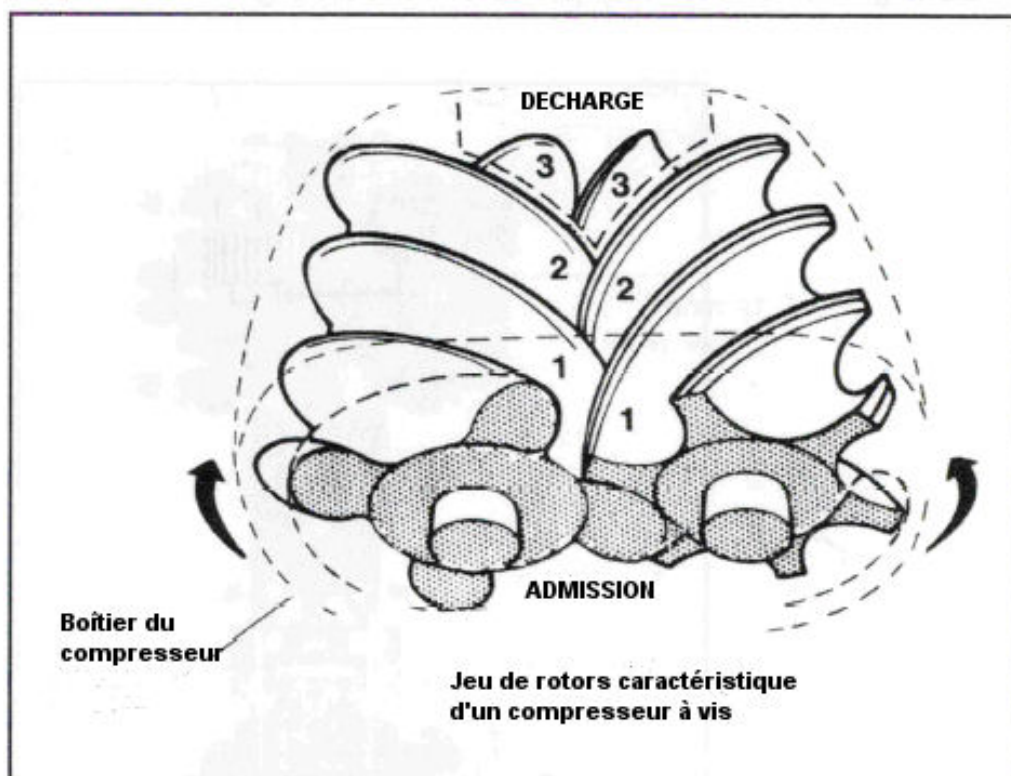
Rotor caractéristique d'un compresseur à vis sans huile
